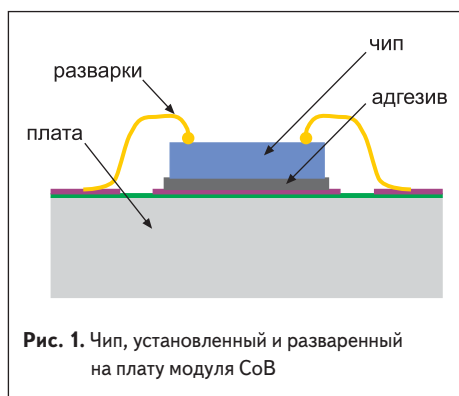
Чип, установленный и разваренный на плату модуля CoB
